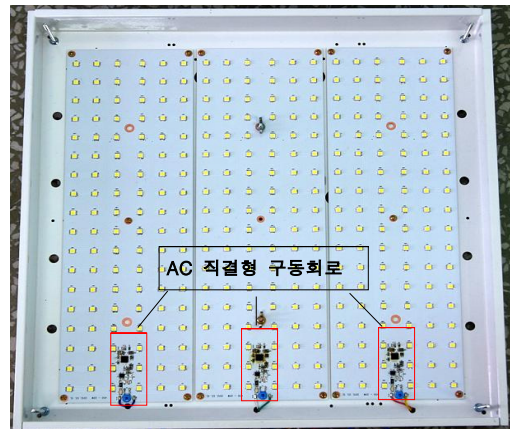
LED 면조명용 AC 직결형 구동기의 PCB 회로
